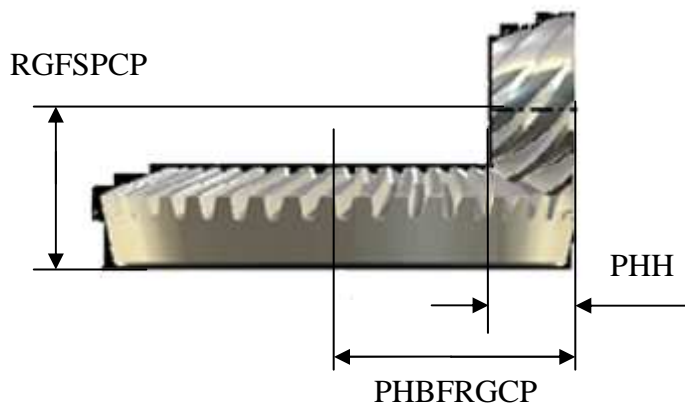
Desenho do gear set com as cotas de montagem.
